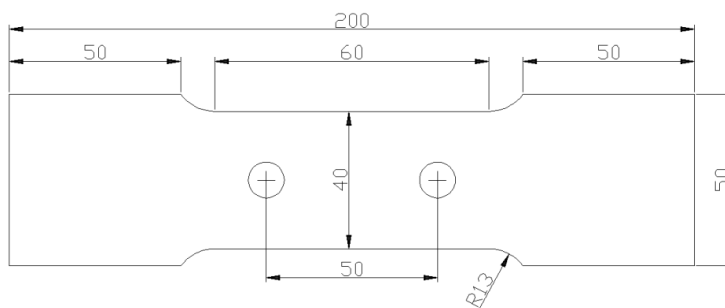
dimensiones de la probeta para ensayo de tracción.
